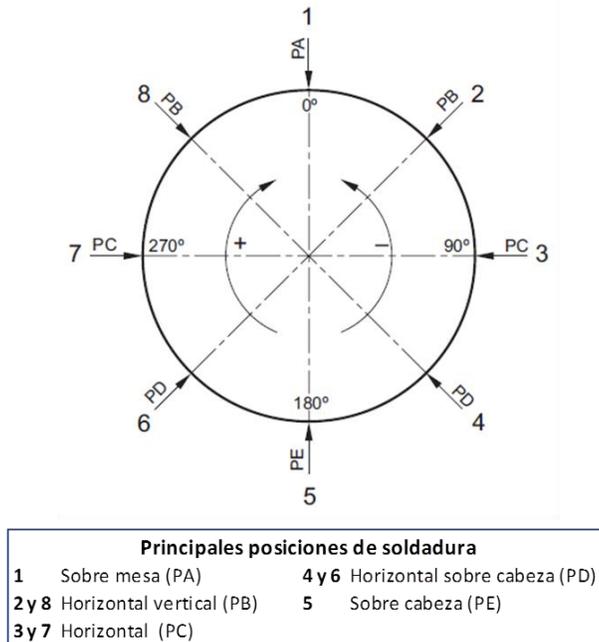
Principales posiciones de soldadura acorde a ISO 6947:2010
